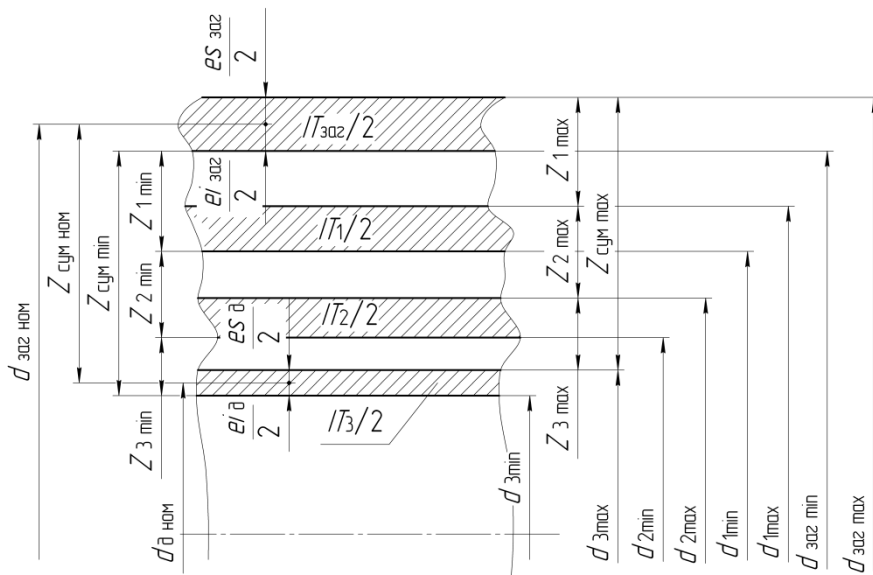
Схема розташування проміжних припусків і допусків на проміжні та початкові розміри заготовки для обробки зовнішньої поверхні обертання лезовими різальними інструментами, встановленими на розмір
